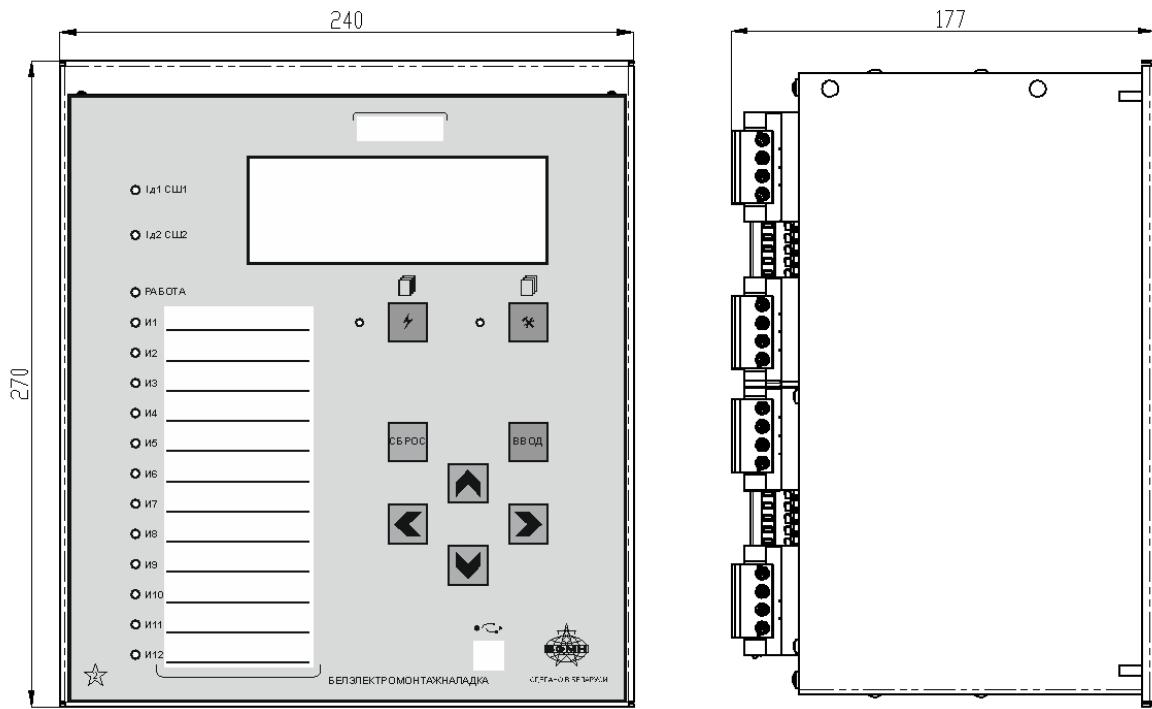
Габаритные размеры MP90x, корпус К2
